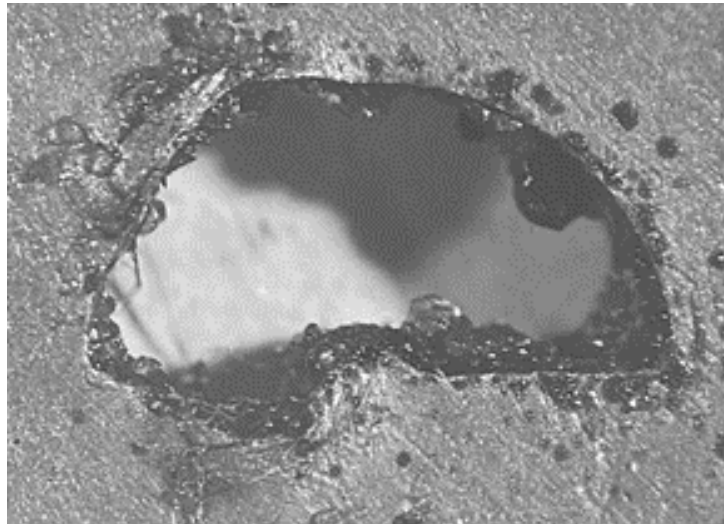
Выступы металла, располагающиеся на технологическом отверстии основного диска
